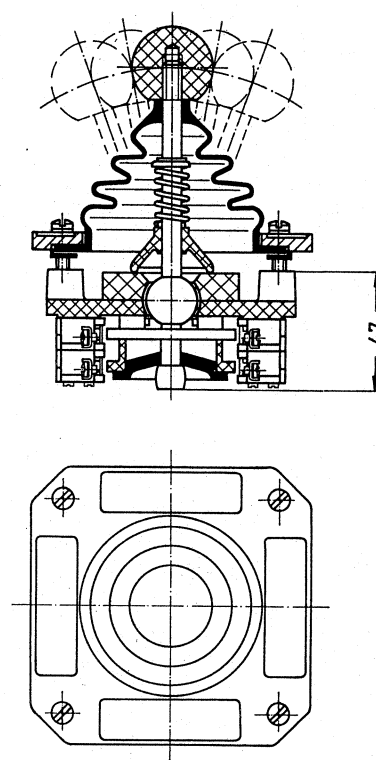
Universal-Steuerschalter, 2-stufige Ausführung,
